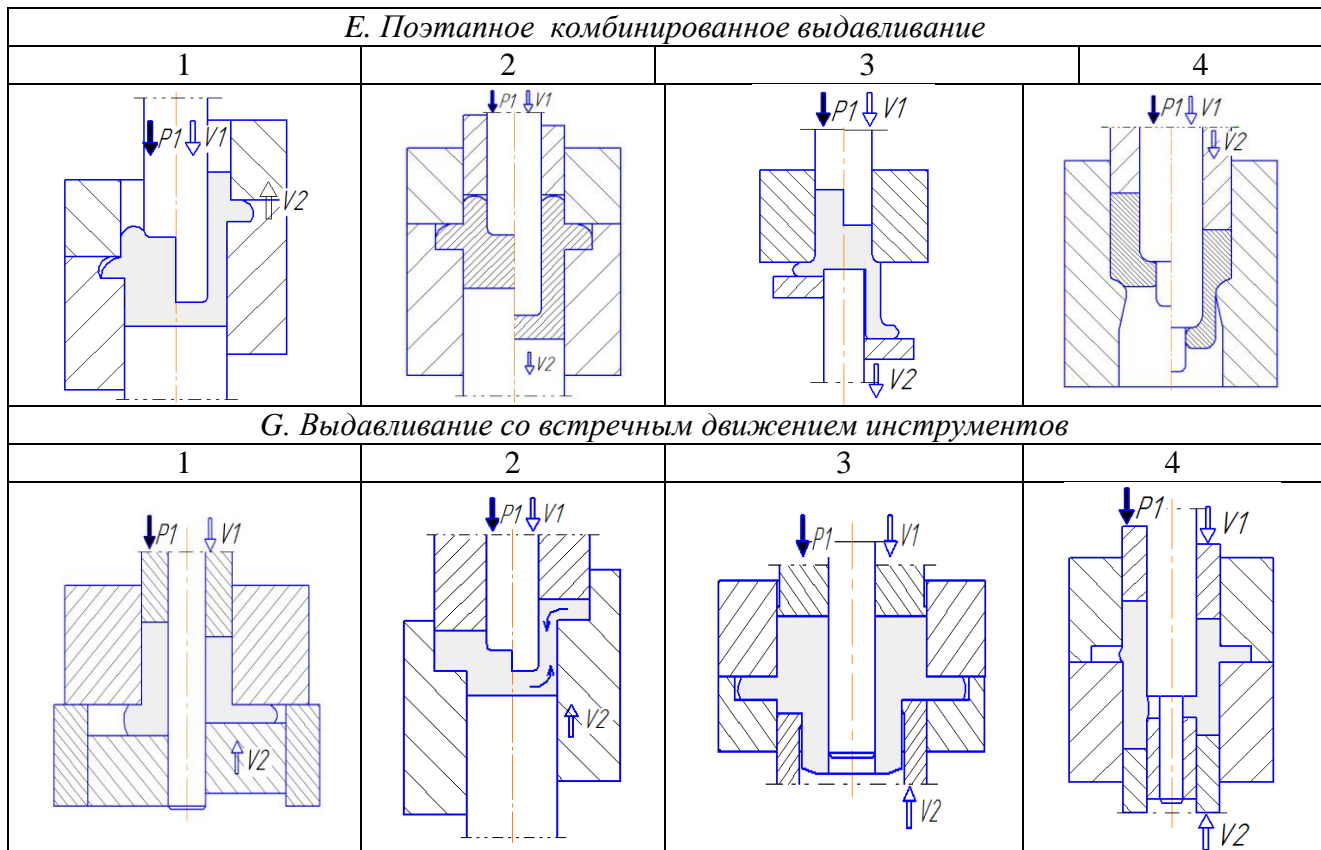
Схемы выдавливания со сложной кинематикой перемещения инструментов
